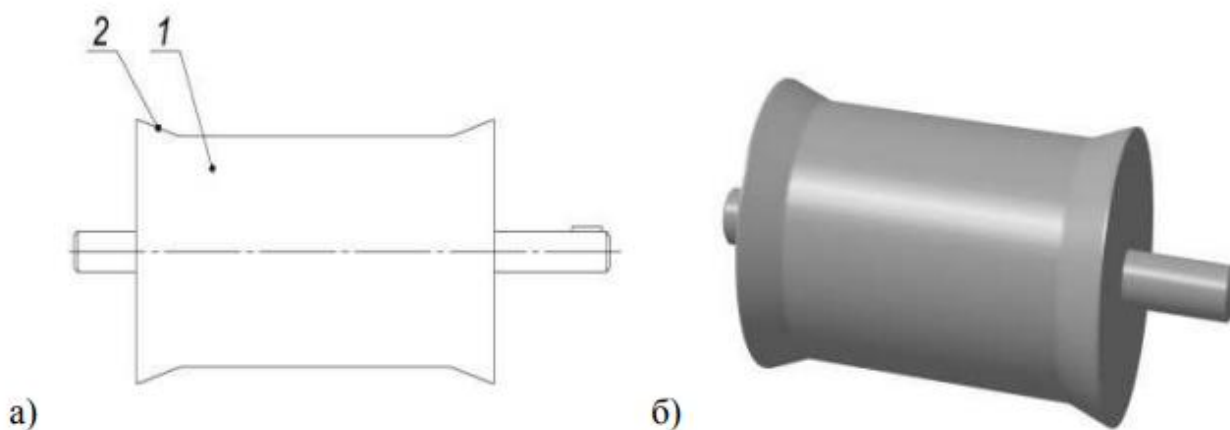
Патент України № UA 3078 Барабан стрічкового конвеєра: а) 2D вид; б) 3D вид; 1- центральна циліндрична ділянка; 2- торцева кінцева ділянка.
